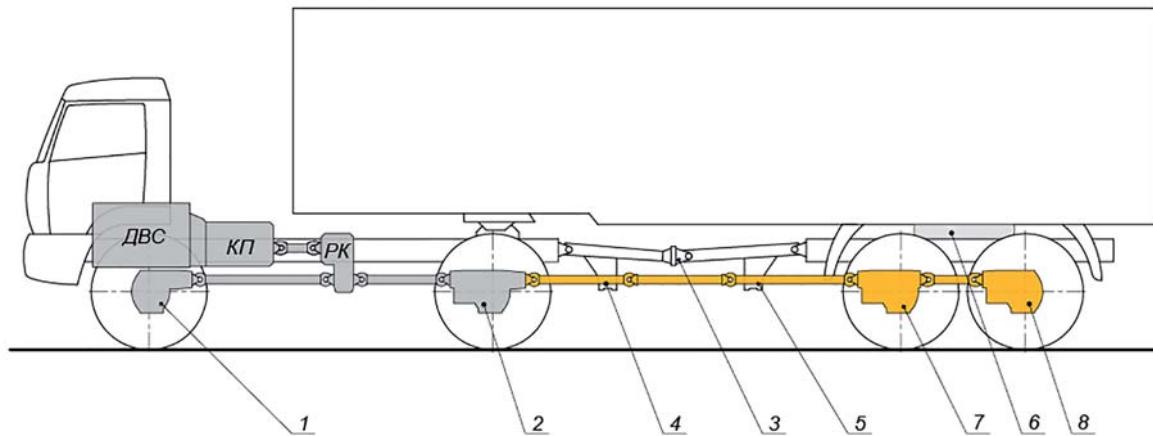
Компоновка агрегатов привода типа «Multidrive»:
